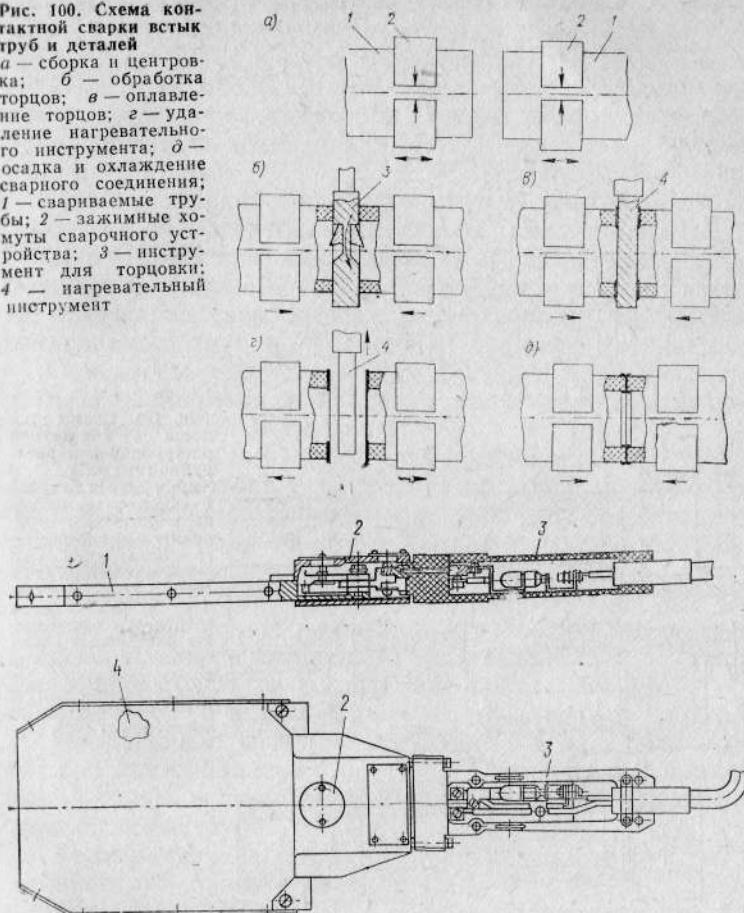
Электронагревательный инструмент для стыковых сварных соединений НСПМ-110
